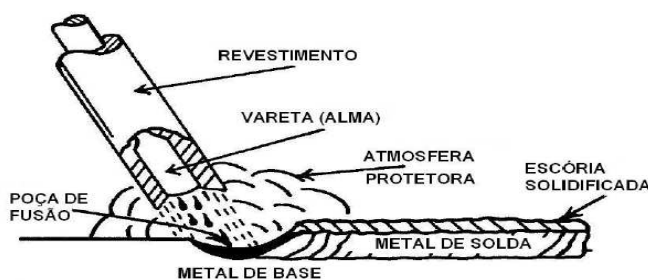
Processo de Soldagem a Arco Elétrico [Fortes, 2005].
